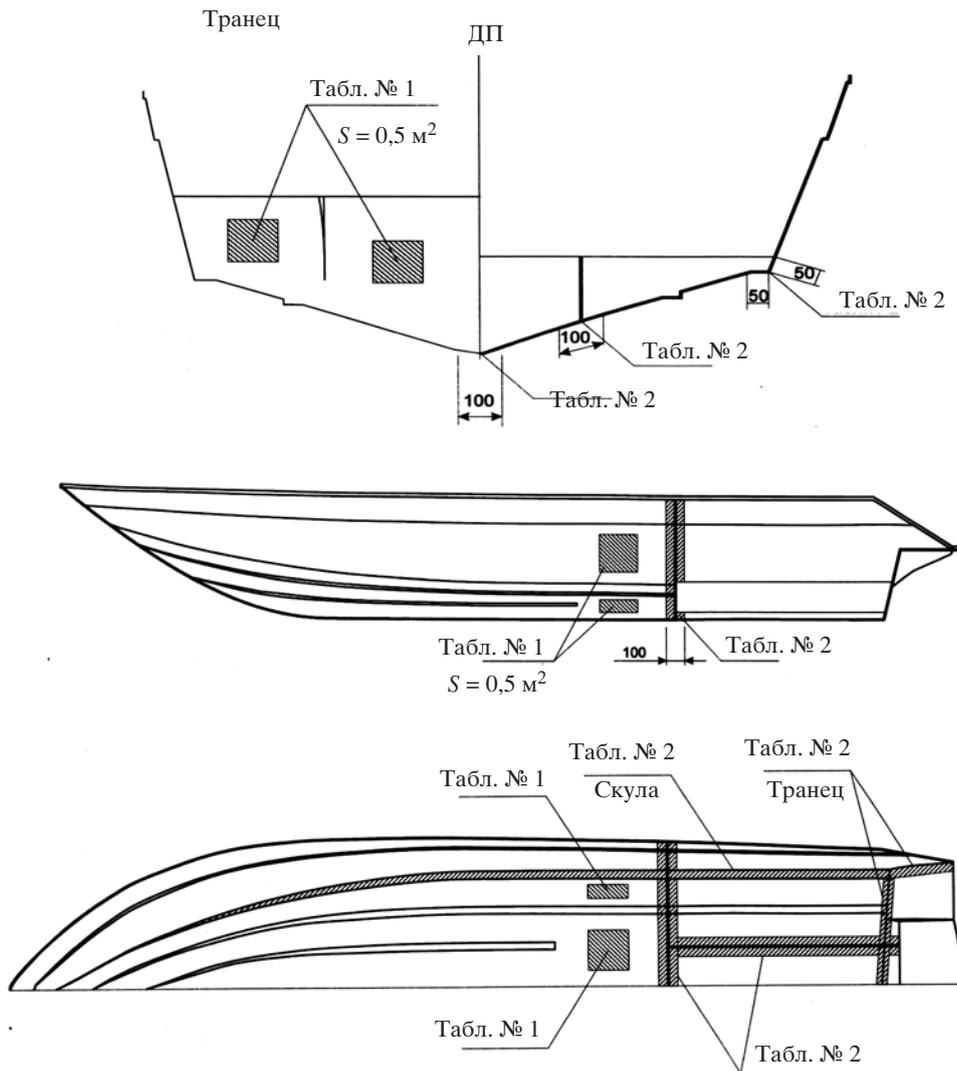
Расположение участков 1-й и 2-й групп конструкций на корпусе судна из композитов.
